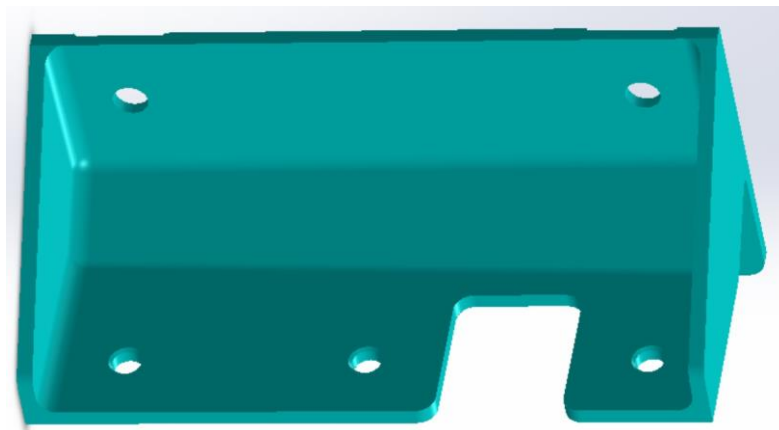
Peça simétrica à utilizada no estudo, injetada também no mesmo molde (THP Brackets G02810036-002).
